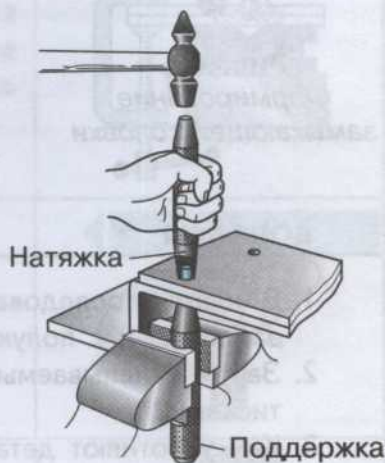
Уплотнение соединяемых деталей с помощью натяжки
